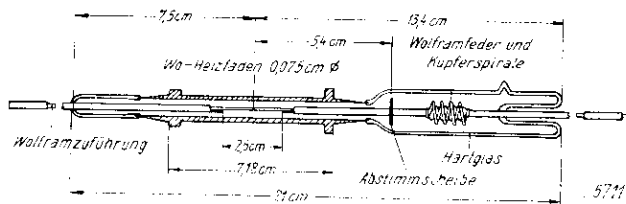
Die Magnetfeldröhre mit ihren Abmessungen
